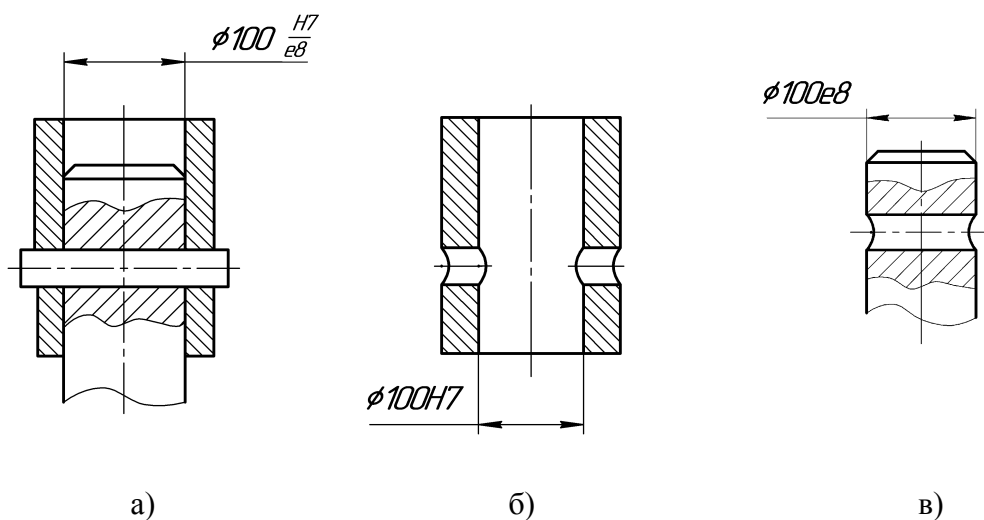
Обозначение допусков на чертеже: а) – фрагмент чертежа общего вида, б) – чертеж втулки с отверстием, в) – чертеж вала с отверстием
